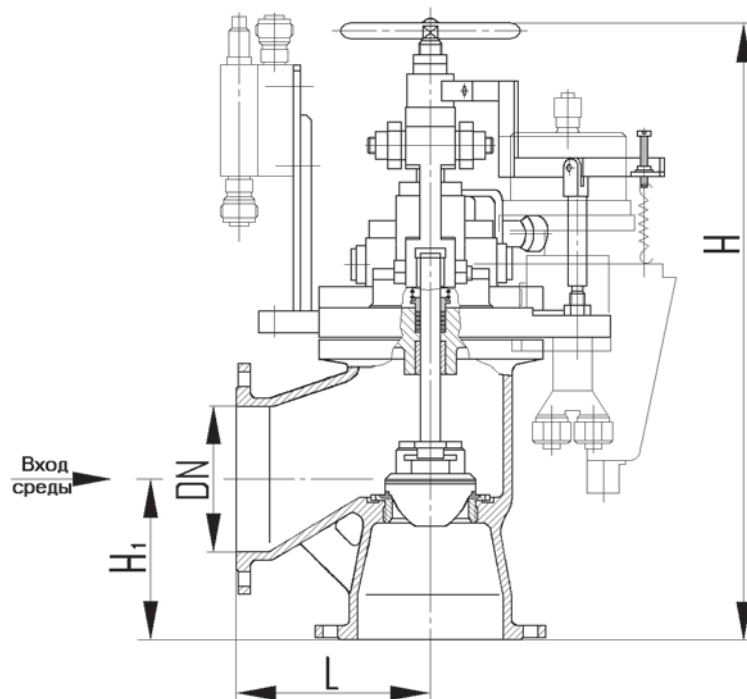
Клапан регулирующий угловой фланцевый с гидроприводом
